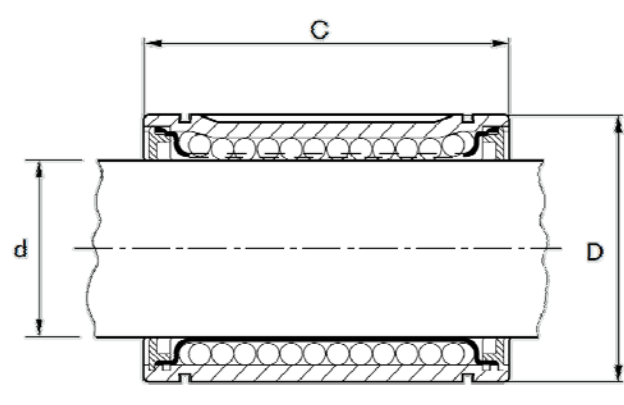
30. Esquema del rodamiento lineal. Fuente: *Rexroth Bosch AG [8]
